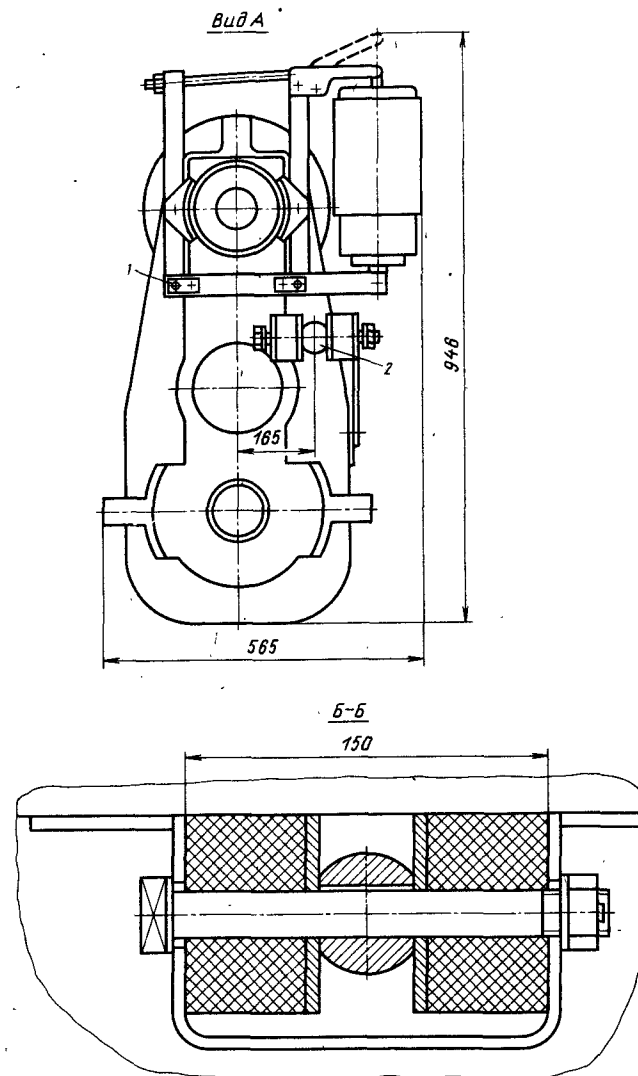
Узел крепления навесного редуктора типа ЦЗ-Вкф
